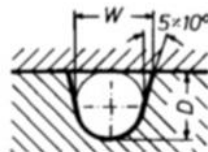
1 Dimensiones del canal trapezoidal modificado
